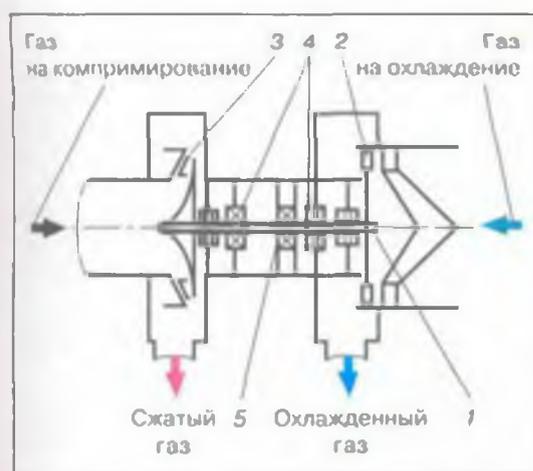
Волновой детандер: 1 – ротор; 2 – газораспределитель расширяемого газа; 3 – газораспределитель компримируемого газа; 4 – подшипники; 5 – магнитная муфта.
